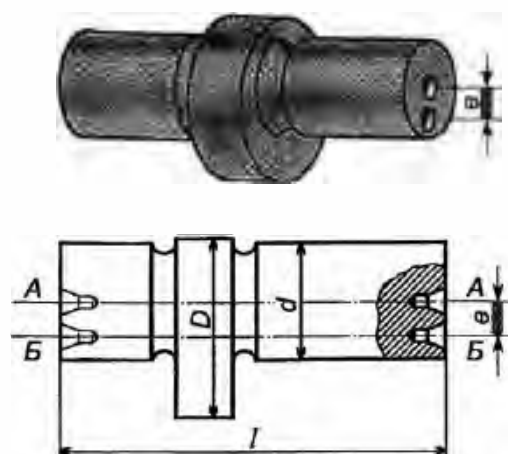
ЕКСЦЕНТРИЧНИЙ ВАЛ
